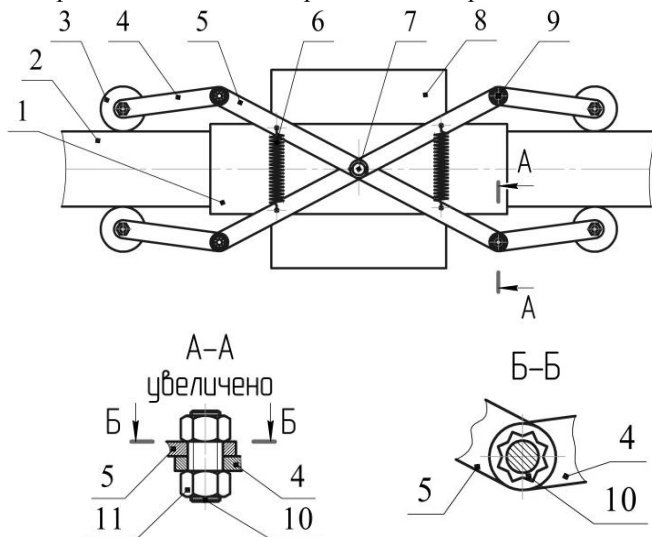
Устройство для обеспечения устойчивости измерительного комплекса: 1 – двухколесная ходовая рама; 2 – рельс; 3 – боковой ролик; 4 – рабочий конец ножниц; 5 – рукоять ножниц; 6 – пружина; 7 – ось ножниц; 8 – противовес; 9 – угловой регулятор; 10 – шлицевой вал; 11 – гайка
